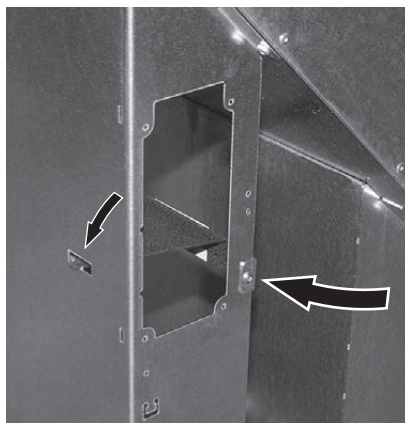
Inserire la linguetta nella cavità e fissare sul davanti con una vite autofilettante – vista da davanti
